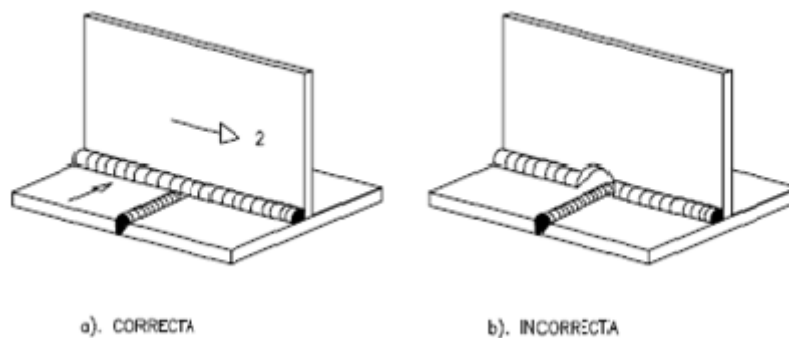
4.3.1.4 Uniones en ángulo con soldaduras cruzadas
